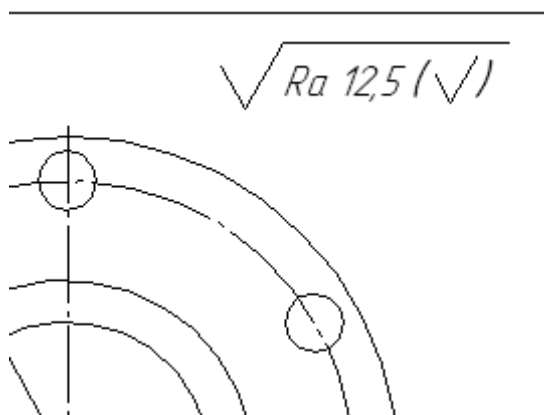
Обозначение неуказанной шероховатости поверхности
